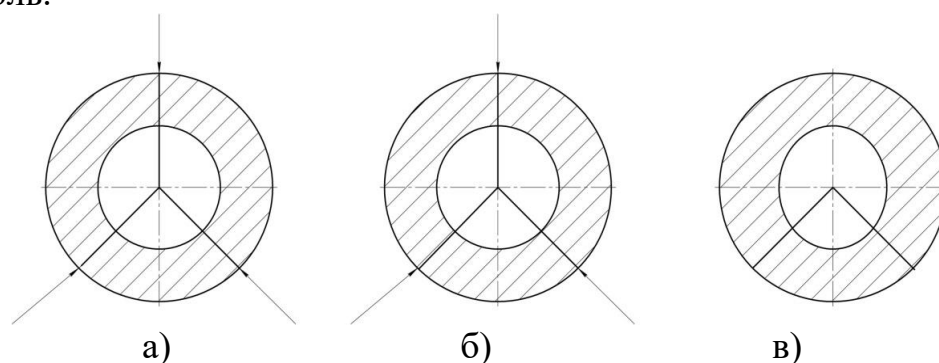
Деформации нежесткой заготовки при её закреплении
